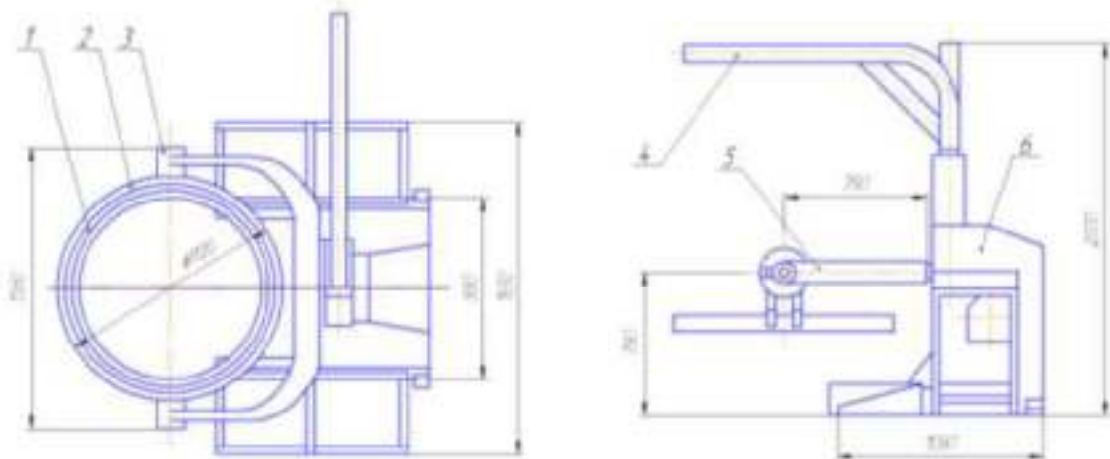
Стенд для разборки и сборки V- образных двигателей (Модель 6501-72)
